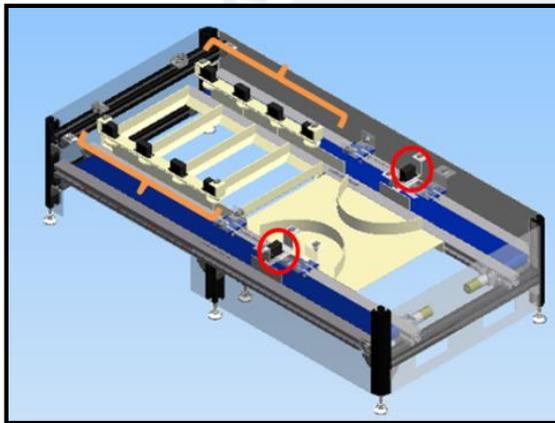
Ubicación de TowerPro MG946R
